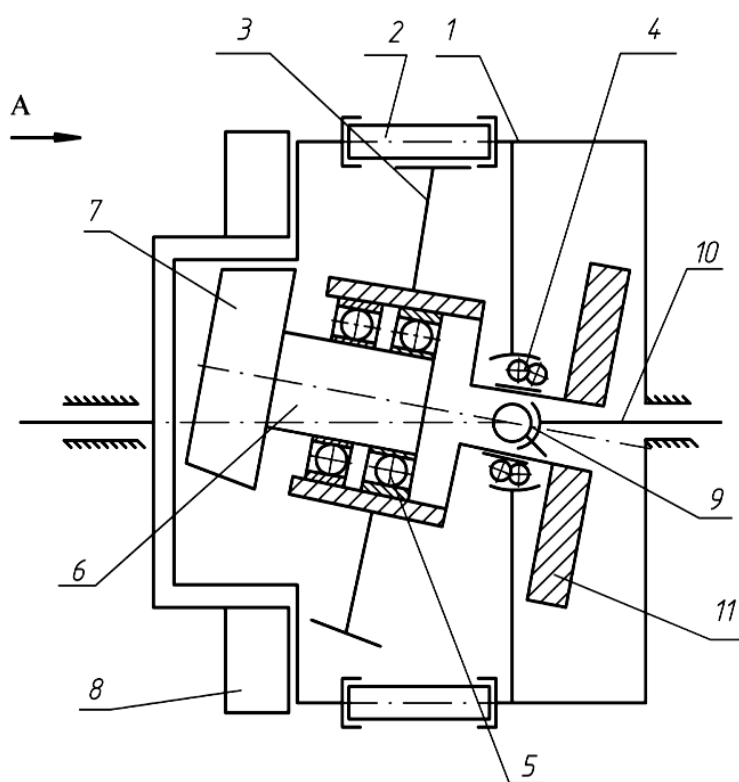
Схема планетарного магнитного привода, разработанная на базе передачи К-Н-V
